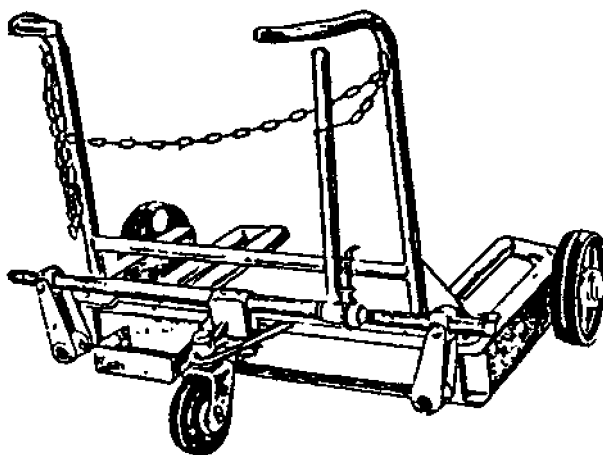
Общий вид тележки П-217 для снятия-установки колес
